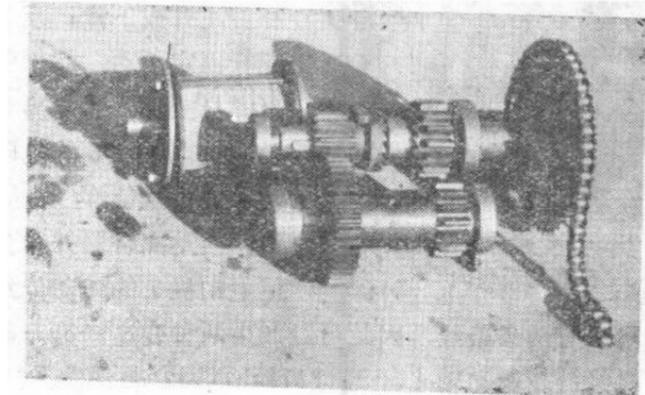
齿轮、链轮、电磁铁等传动零件的组装
